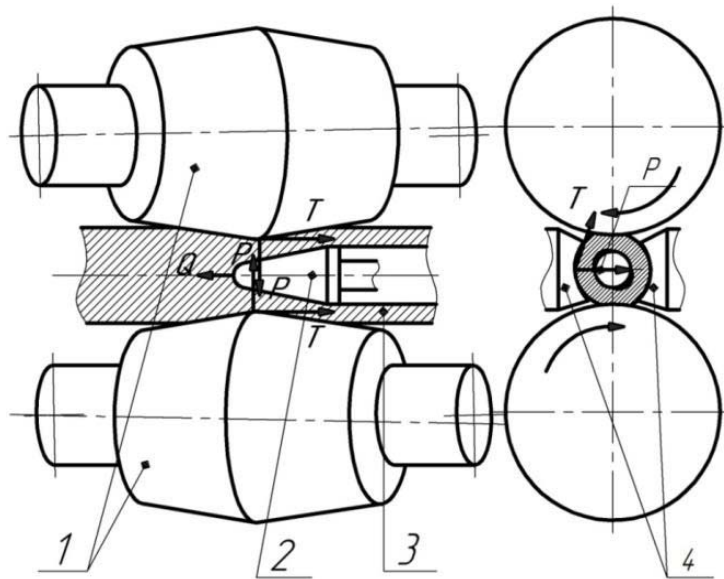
Схема очага деформации при прошивке в станах винтовой прокатки:
